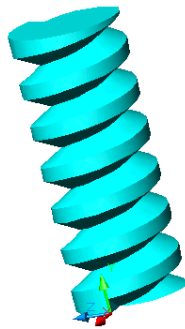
Drej koordinatsystemet ved at venstreklikke indtil det er placeret som vist på denne figur. Planet bliver dit nye skitseplan.
